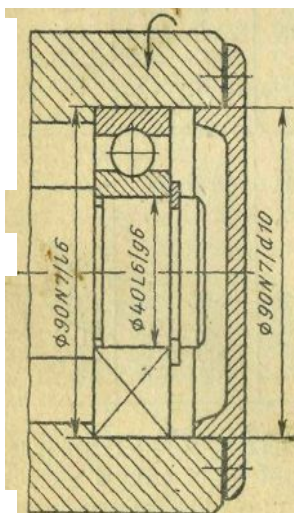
Пример обозначения посадок на сборочном чертеже подшипникового узла..
